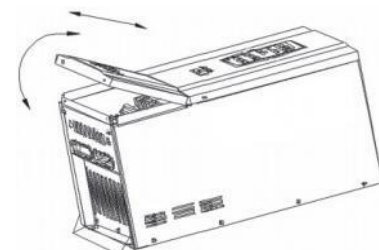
Diagrama de desmontaje de la placa de cubierta inferior de la carcasa de chapa metálica
